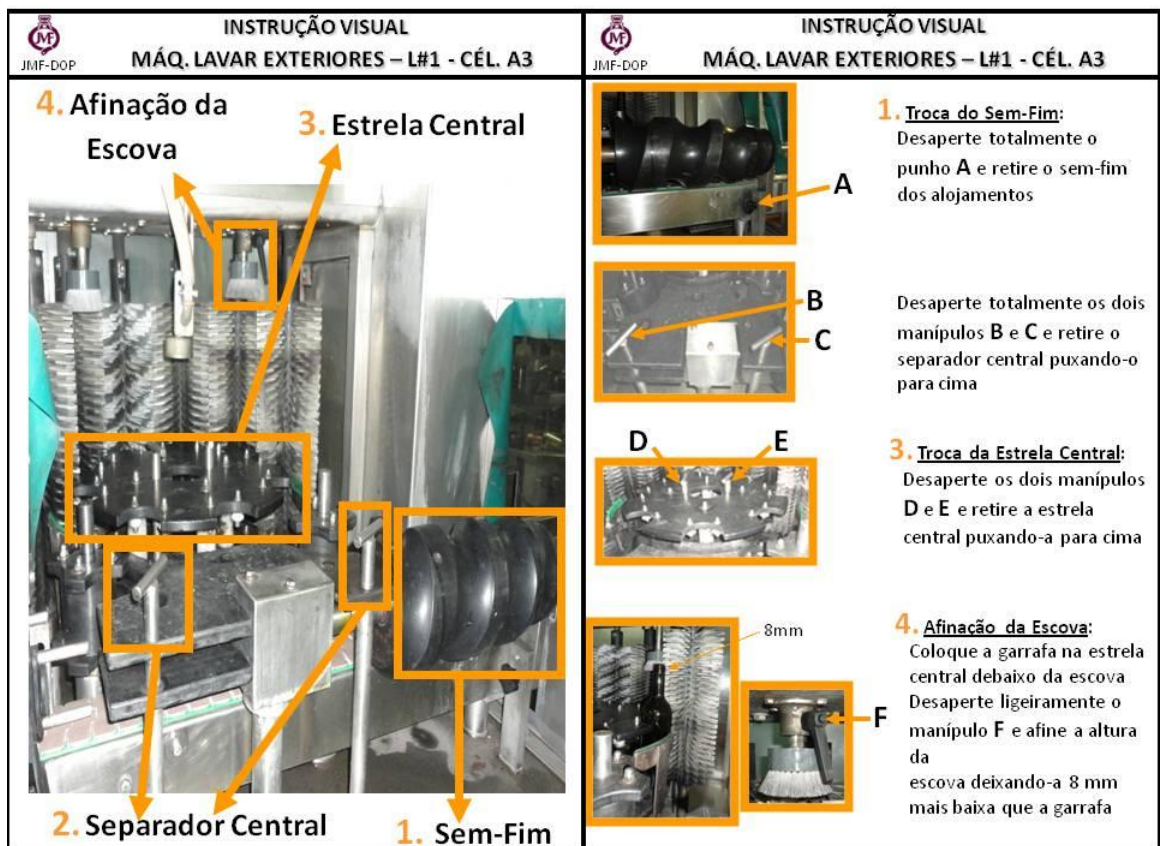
Instrução Visual do Equipamento de Lavagem de Exteriores
